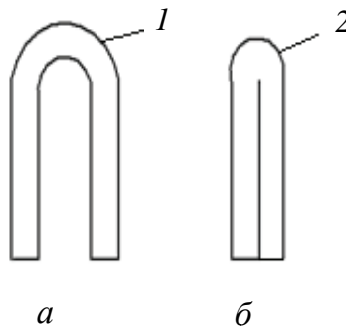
Подготовка образца для сварки: 1, 2 – зона выполнения шва
